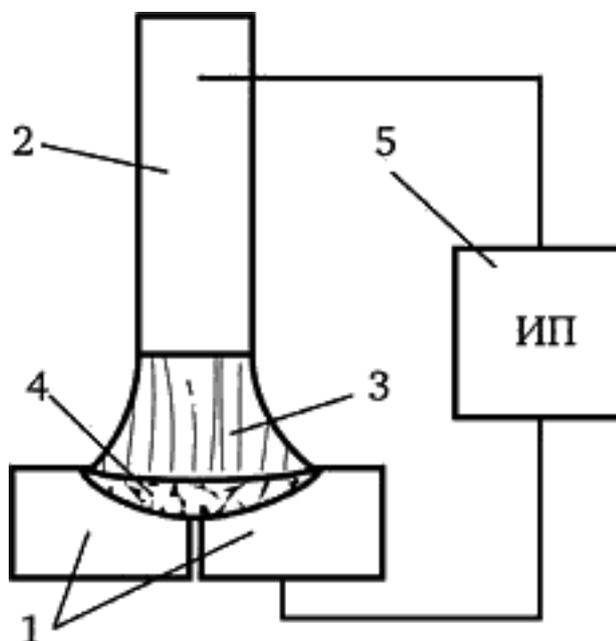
Электрическая сварочная цепь дуговой сварки:
